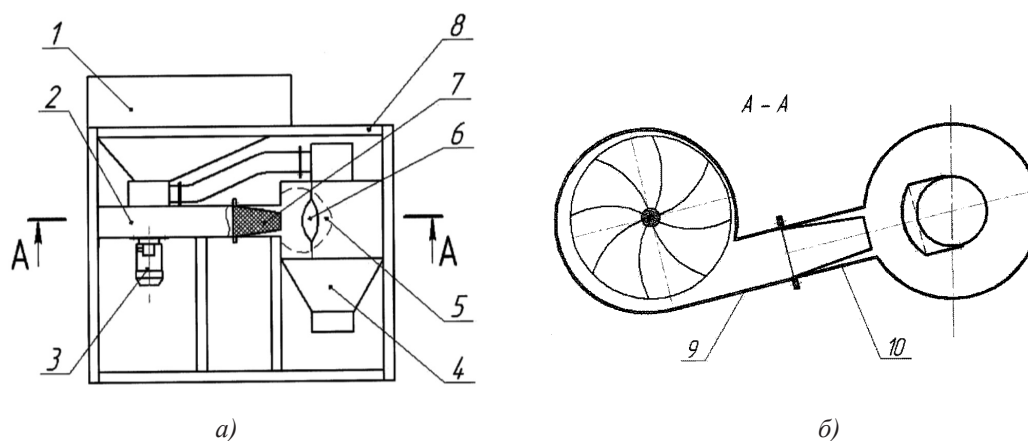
Устройство для снятия плодовых оболочек с зерна: а) – общий вид устройства; б) – разрез А-А; 1 – бункер питающий; 2 – вентилятор; 3 – электродвигатель; 4 – осадитель; 5 – труба вытяжная; 6 – сферическая рабочая пластина; 7 – сетчатый рабочий орган; 8 – рама; 9 – выходной патрубок вентилятора; 10 – входной патрубок осадителя
